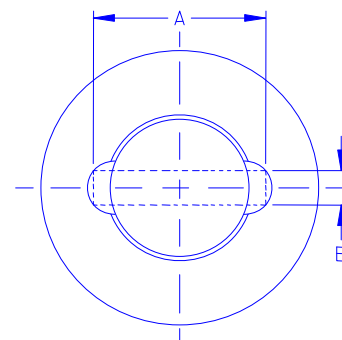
Abmessungen für Sicherungsring-Ausbauwerkzeug
